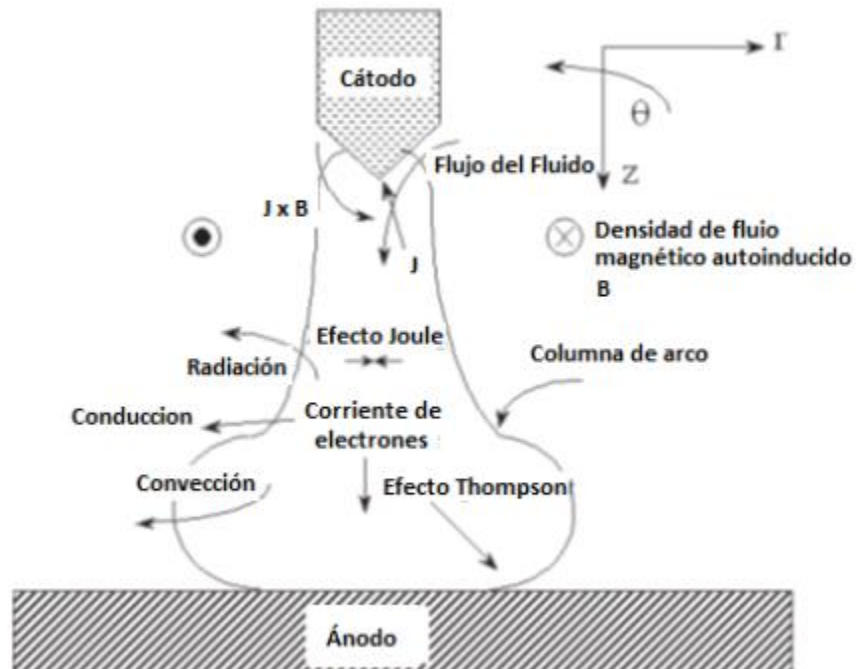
Esquema de una soldadura GTAW con los procesos involucrados en la soldadura.
